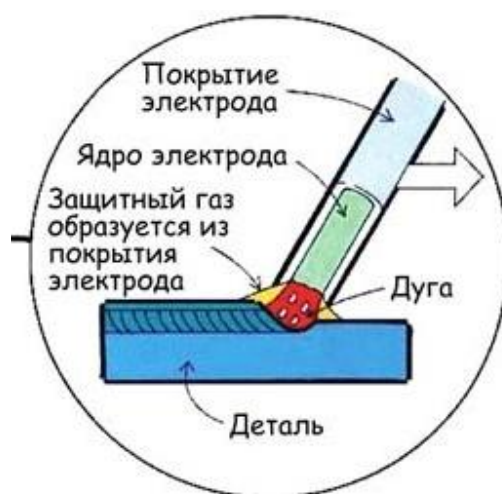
Дуговая сварка штучными электродами
